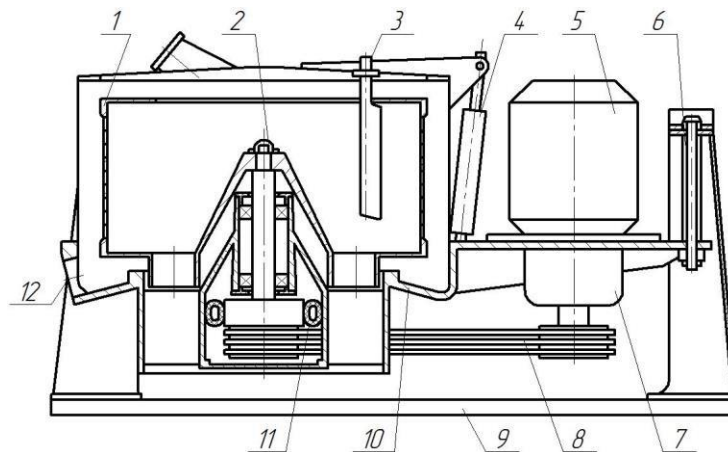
Схема центрифуги типу ФМБ: 1 – ротор; 2 – вал ротора; 3 – ввідний штуцер; 4 – механізм підйому кришки; 5 – електропривід; 6 – колонна з пружинами; 7 – гідромуфта; 8 – клиноремінна передача; 9 – фундаментна плита; 10 – кожух; 11 – гальмівний механізм; 12 – зливний штуцер
